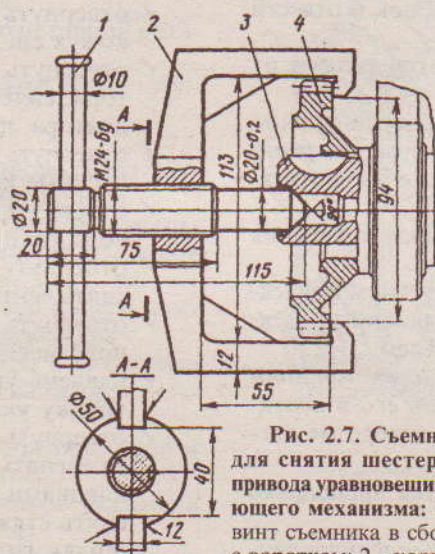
Съемник для снятия шестерни привода уравновешивающего механизма: 1 – винт съемника в сборе с воротком; 2 – корпус съемника; 3 – коленчатый вал; 4 – шестерня
